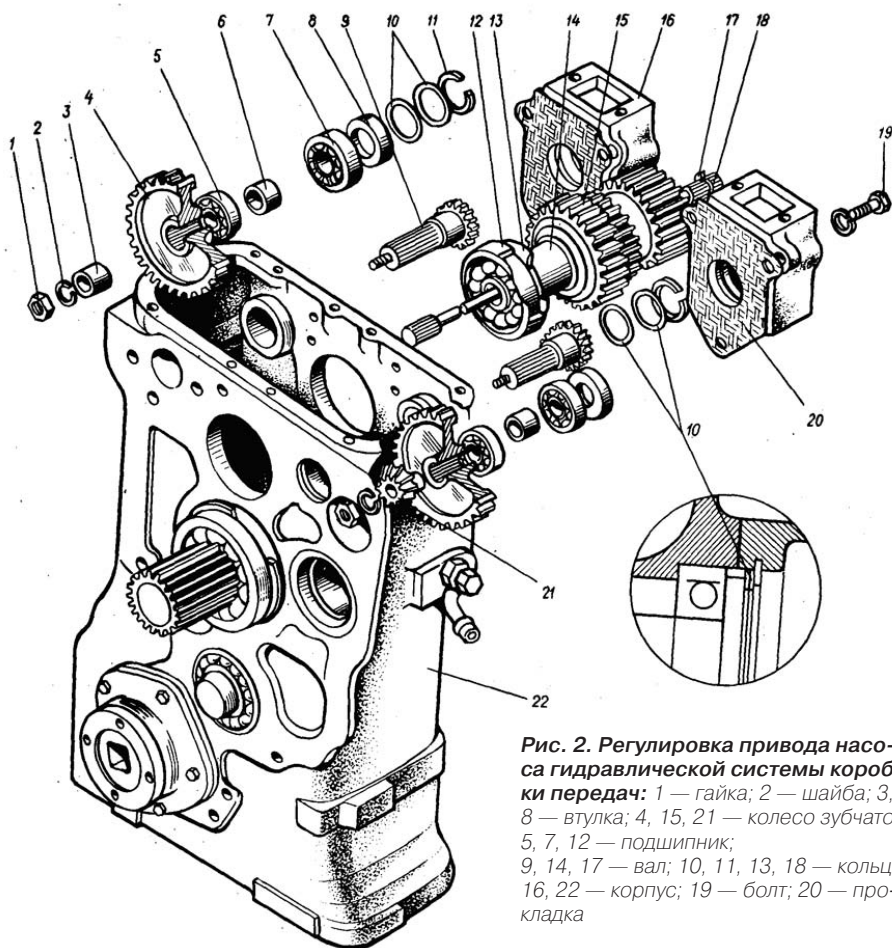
Регулировка привода насоса гидравлической системы коробки передач: 1 — гайка; 2 — шайба; 3, 6, 8 — втулка; 4, 15, 21 — колесо зубчатое; 5, 7, 12 — подшипник; 9, 14, 17 — вал; 10, 11, 13, 18 — кольцо; 16, 22 — корпус; 19 — болт; 20 — прокладка
